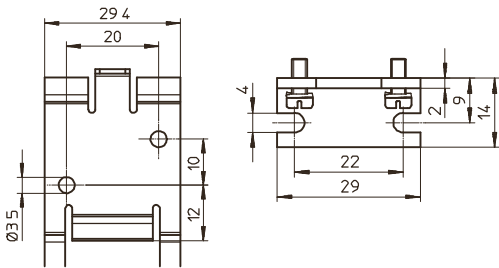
Слева – крепление на стену, справа – крепежный уголок
